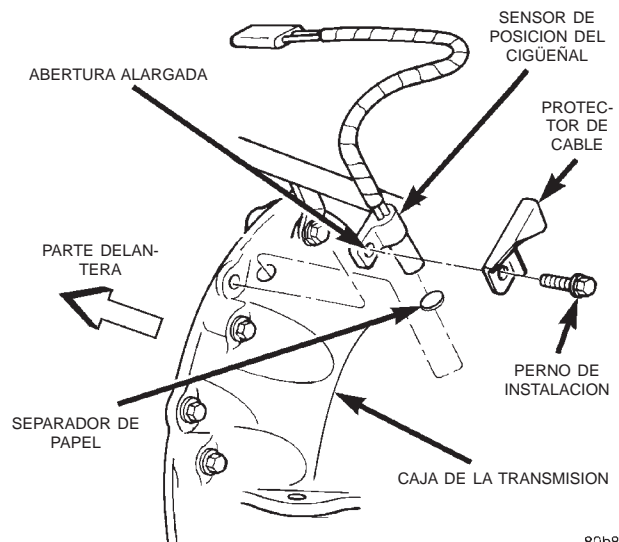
Sensor de CKP—motor 4.0L de 6 cilindros
